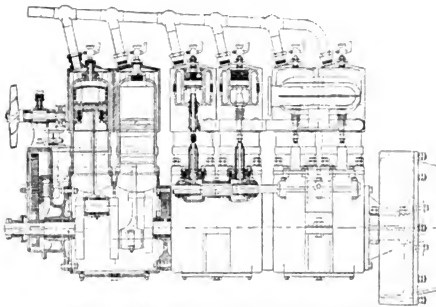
Sechszylinder-Hexe-Motor; im Längsschnitt.
